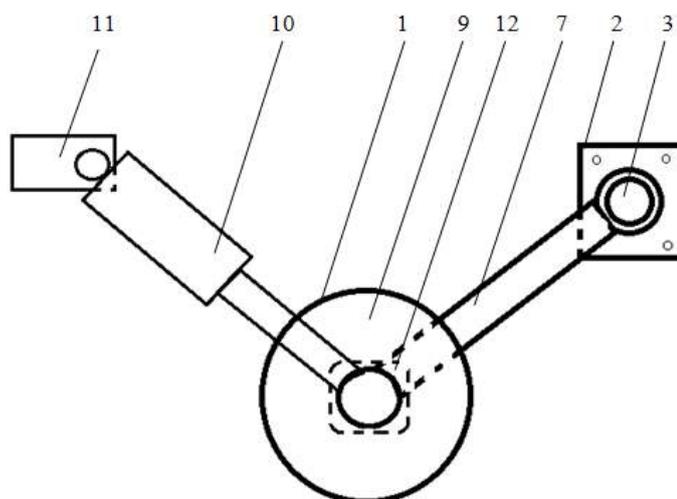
а - Принципиальная схема гидроприжимного дискарного почвенного разуплотнителя (1 - общий вид разуплотнителя, 2 - косыночные упоры, 3 - силовой шарнир, 4 - рама, 5 - трактор, 6 - колёсные движители, 7 - реактивные штанги, 8 - торсионная ось, 9 - рабочие органы-дискатеры, 10 - силовой гидроцилиндр, 11-кронштейн, 12-вилка рабочей части гидроцилиндра)
